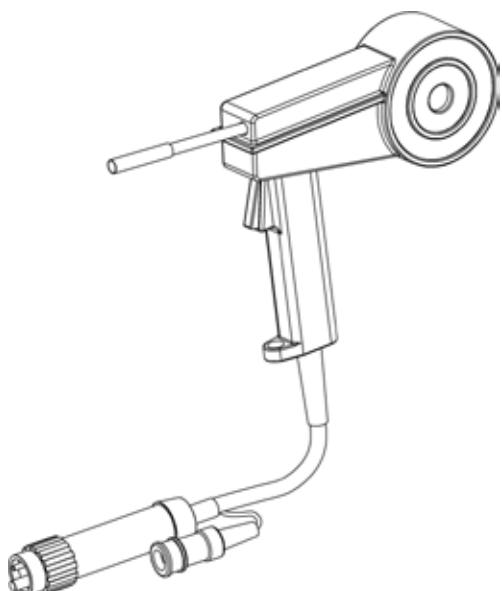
Горелка для MIG сварки типа «Spool gun».
